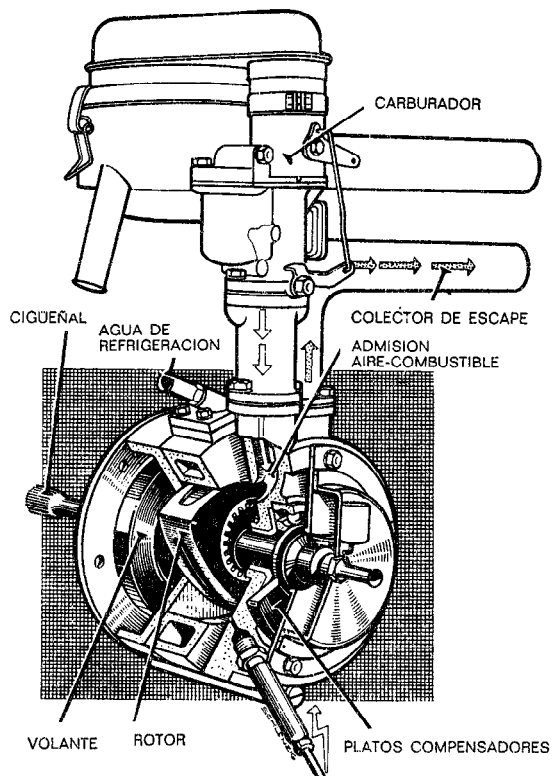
Corte en perspectiva de un motor Wankel.
